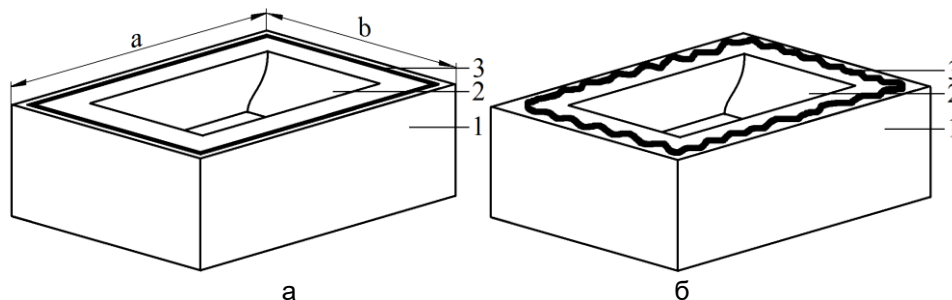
Схема нанесення прямолінійного (а) і зигзагоподібного (б) клейового шва на сполучаються частини форми: 1 – пів-форма; 2 – робоча порожнина пів-форми; 3 – клейовий шов
